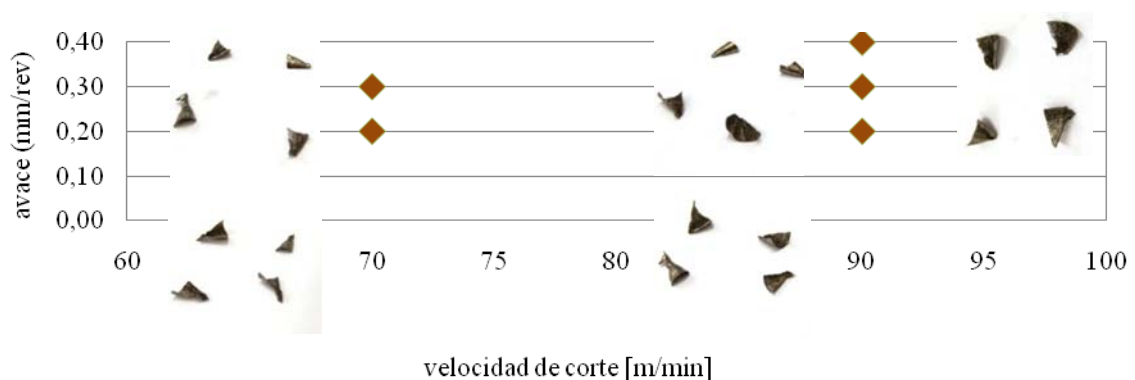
Virutas para diferentes condiciones de corte en fundición nodular GGG70.
